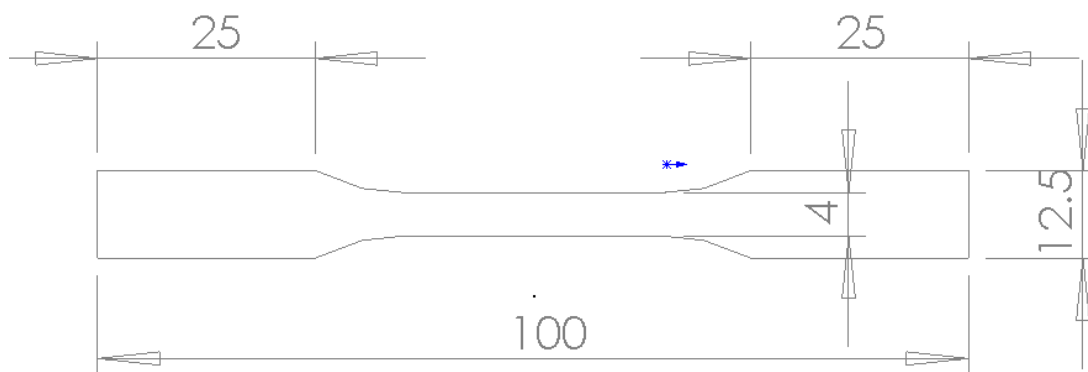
Чертеж образца для проведения испытаний на растяжение
